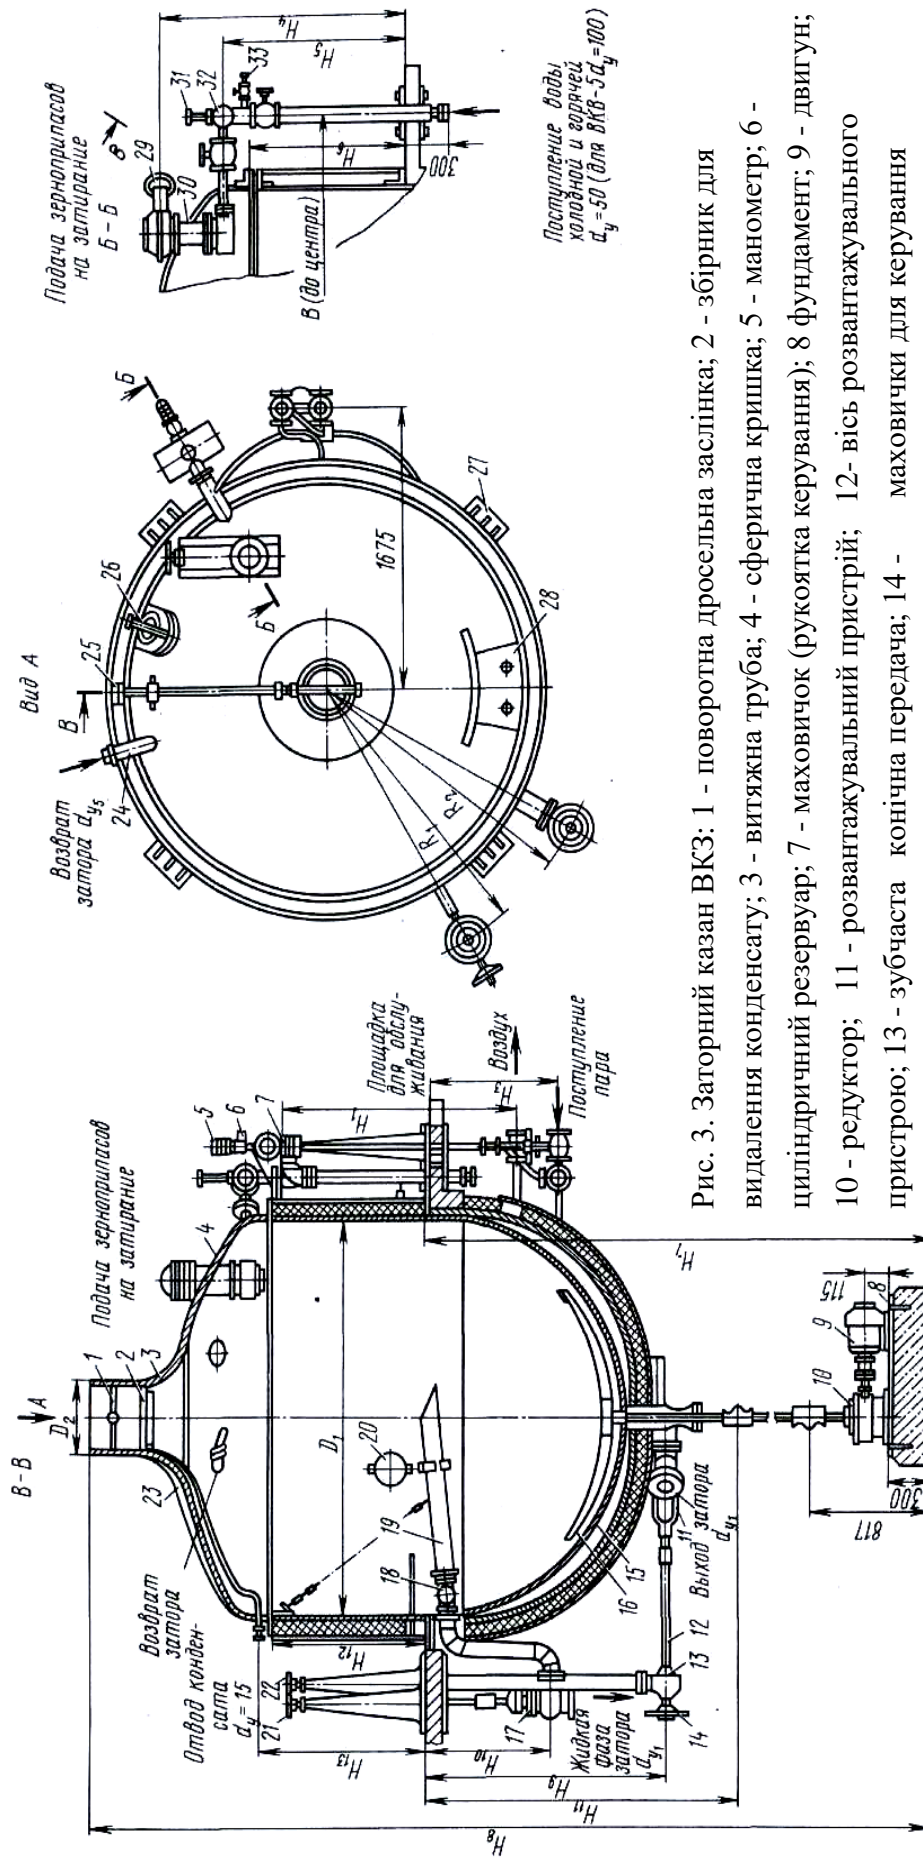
Заторный казан ВКЗ: 1 - поворотна дросельна заслінка; 2 - збірник для видалення конденсату; 3 - витяжна труба; 4 - сферична кришка; 5 - манометр; 6 - циліндричний резервуар; 7 - маховичок (рукоятка керування); 12- вісь розвантажувального 10 - редуктор; 11 - розвантажувальний пристрій; 13 - маховичок (рукоятка керування); 14 - маховичок для керування розвантажувальним пристроєм; 15 - подвійне сферичне днище; 16 - пропелерна мішалка; 17 - запірний пристрій; 18 - шарнір; 19 - стяжна труба; 20 - поплавець; 21 - маховичок для керування запірним пристроєм; 22 маховичок для керування розвантажувальним пристроєм; 23 - труба для видалення конденсату; 24 - патрубок для повернення затопу; 25 - маховичок для повороту пропелерної заслінки; 26 т
